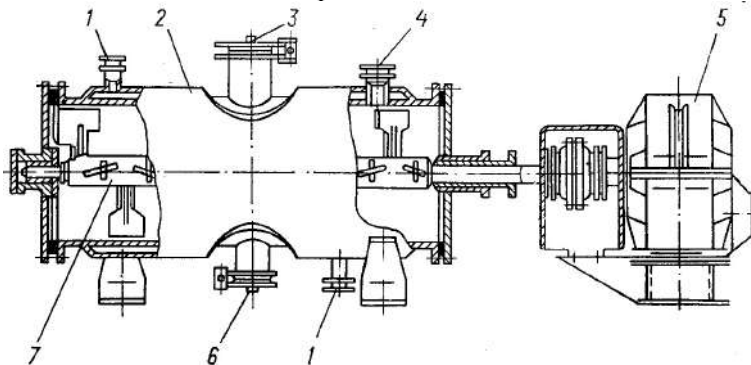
Барабанная вакуумная гребковая сушилка с реверсным вращением ротора: 1 – штуцера для ввода греющего пара и вывода конденсата; 2 – корпус; 3 – загрузочный штуцер; 4 – штуцер для отвода паров; 5 – электродвигатель; 6 – разгрузочный штуцер; 7 – лопастной вал.
